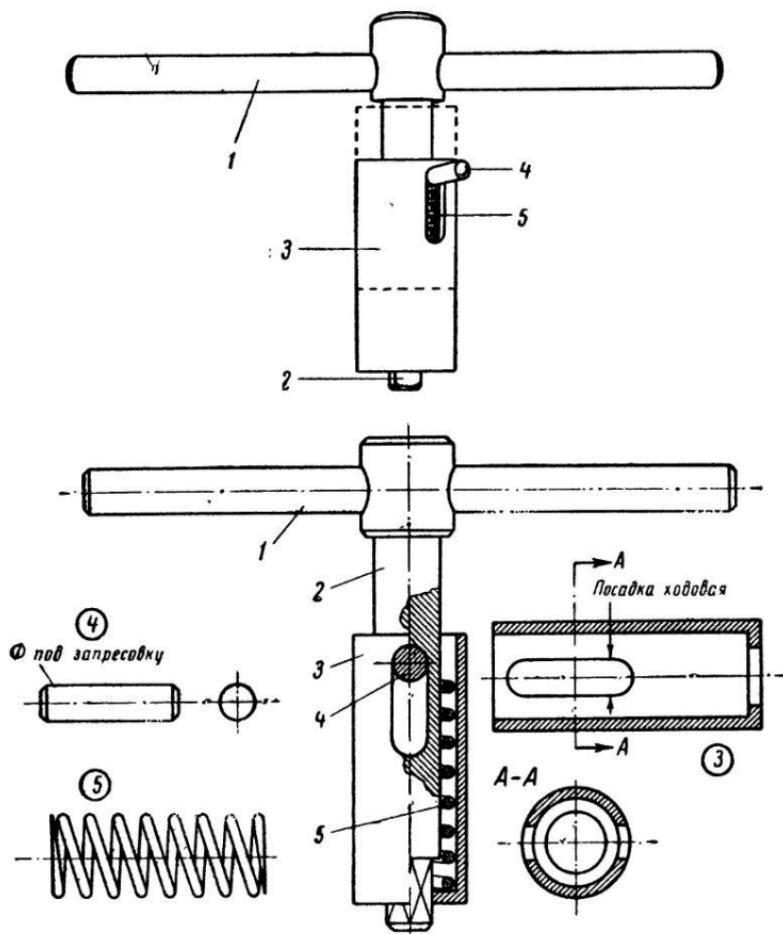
Безопасный ключ для токарного станка и его детали: 1 — ручка; 2 — ключ; 3 — втулка; 4 — штифт; 5 — пружина.
